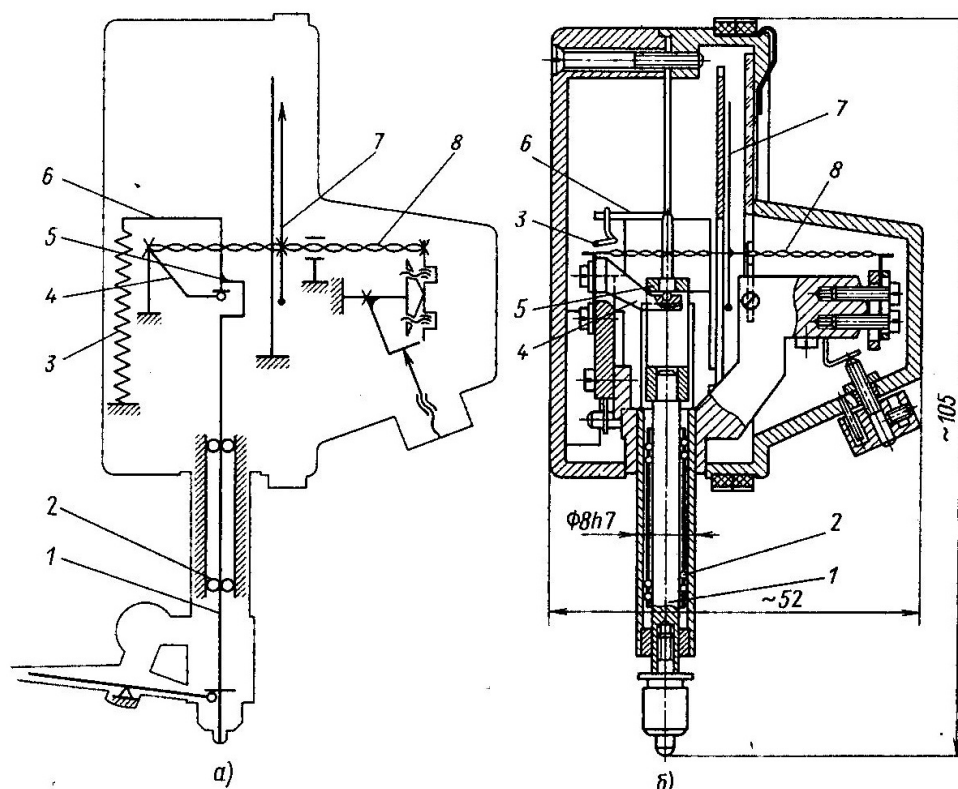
Пружинная малогабаритная измерительная головка-микатор: а – схема; б – конструкция
